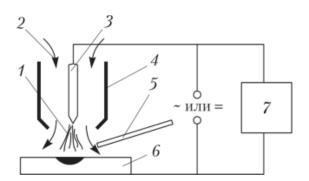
Схема процесса сварки в защитных газах неплавящимся электродом
